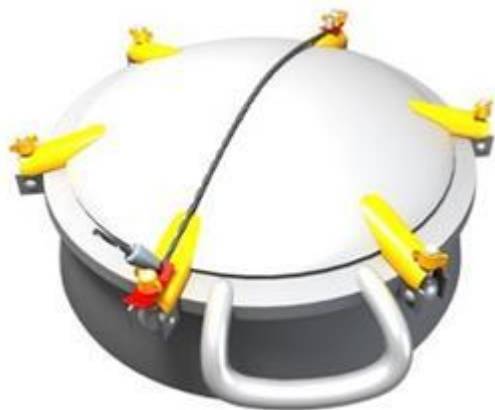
Схема установки универсального ЗПУ с длиной каната 800 и 850 мм на верхней крышке загрузочного люка цистерны барашкового типа, оборудованной «ограничителем хода»
